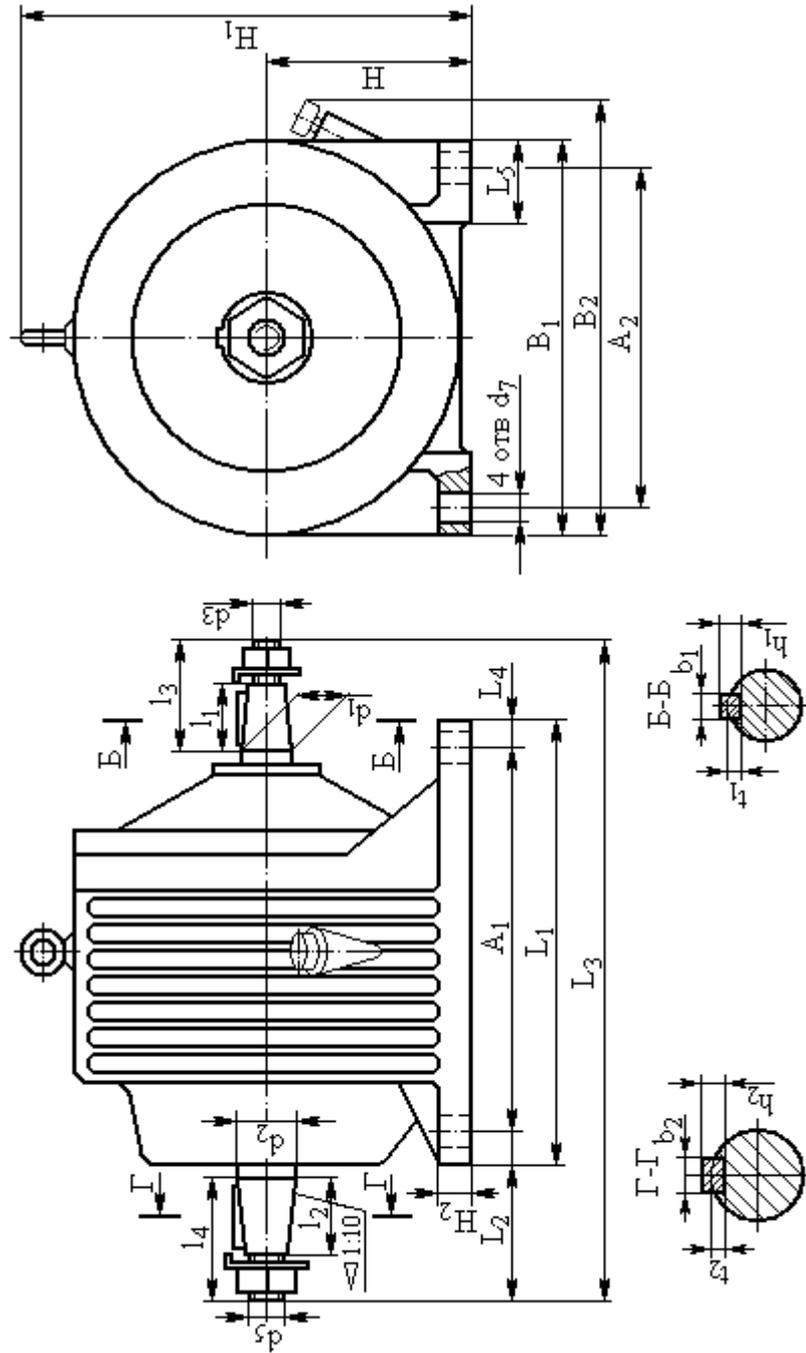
Редуктор планетарный зубчатый двухступенчатый типа Пз2
